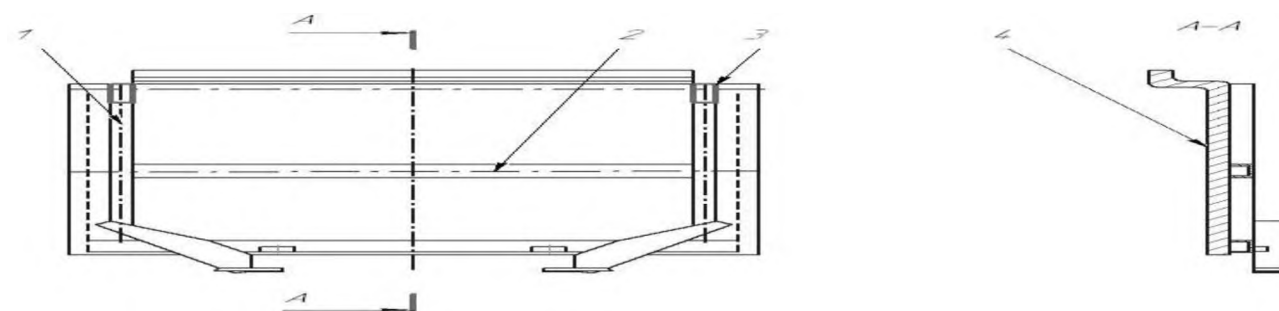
Новая конструкция крышки люка универсального полувагона:
